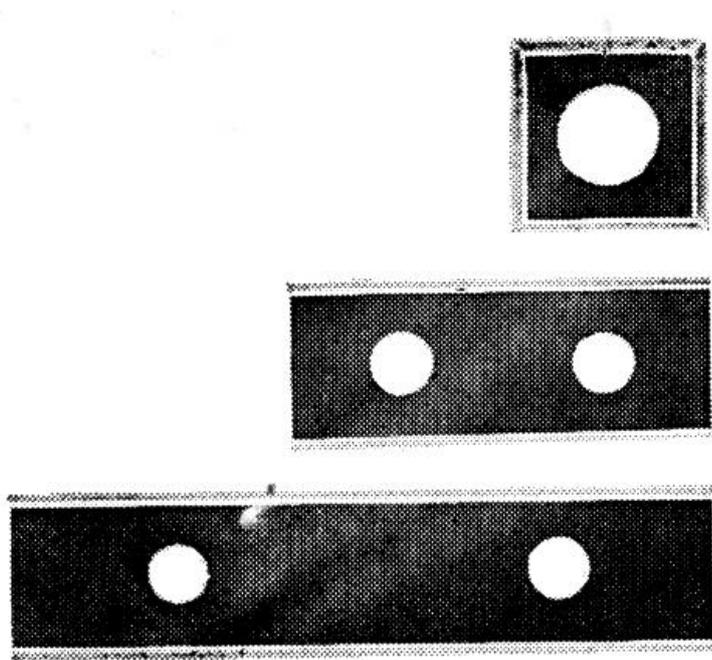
Сплошные поворотные твердосплавные пластинки иностранных фирм.
